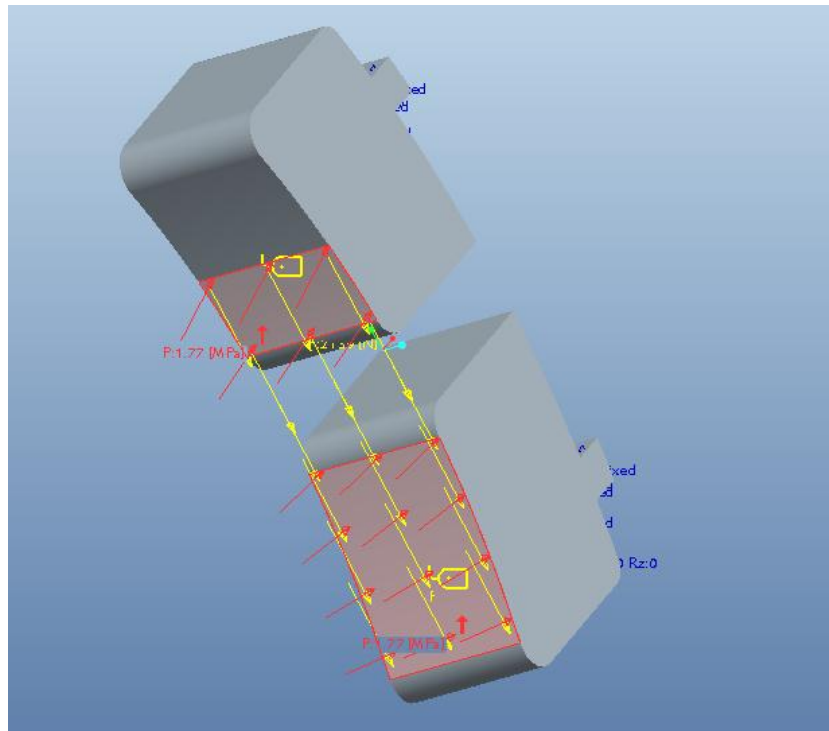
Distribución de cargas con plano en llanta en el extremo superior del ferodo doble de la mitad superior.
